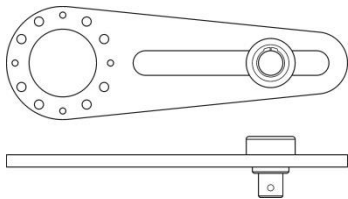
Reacção típica com 'dispositivo slave' deslizante para PT1 a PT5
